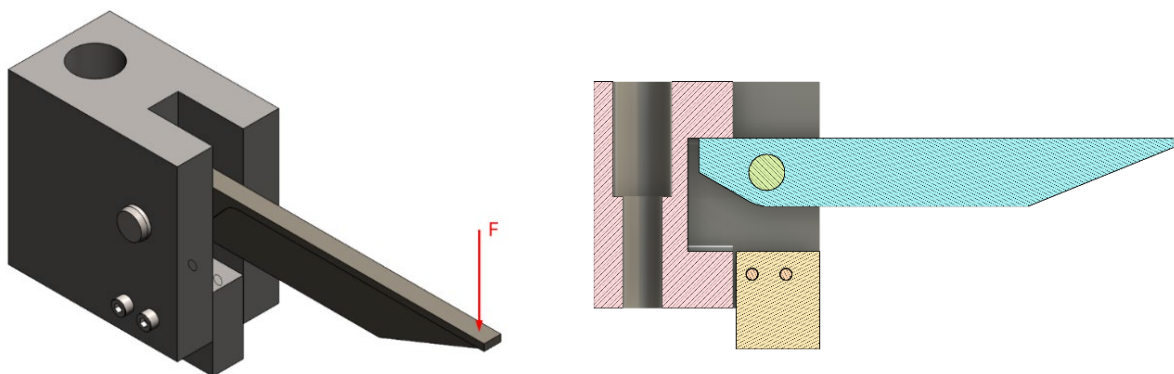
Adapter zur Biegeprüfung des Hebels auf der Druckmaschine - Isometrische Ansicht mit Kraftangriffspunkt am Ende des Hebels (links), Schnitt durch den Adapter mit Lagerauge und Widerlager am Hebel (rechts)
